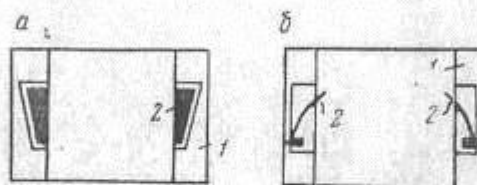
Кольцевой: 1 — корпус, 2 — кольцо;
